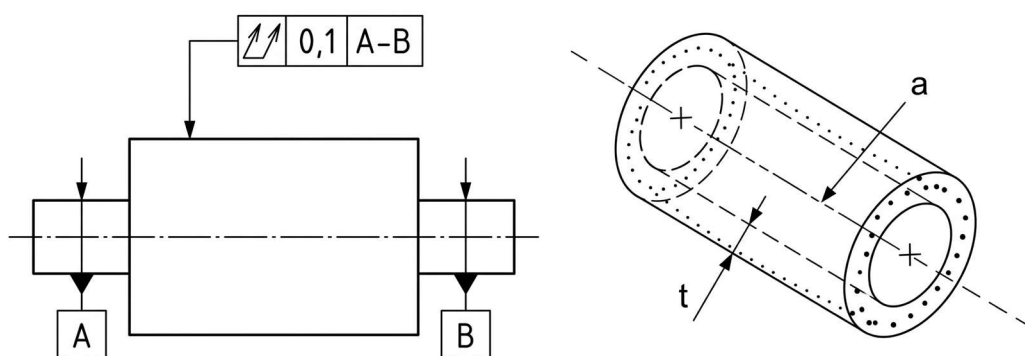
Indikace kruhového obvodového házení a její toleranční pole [8]
